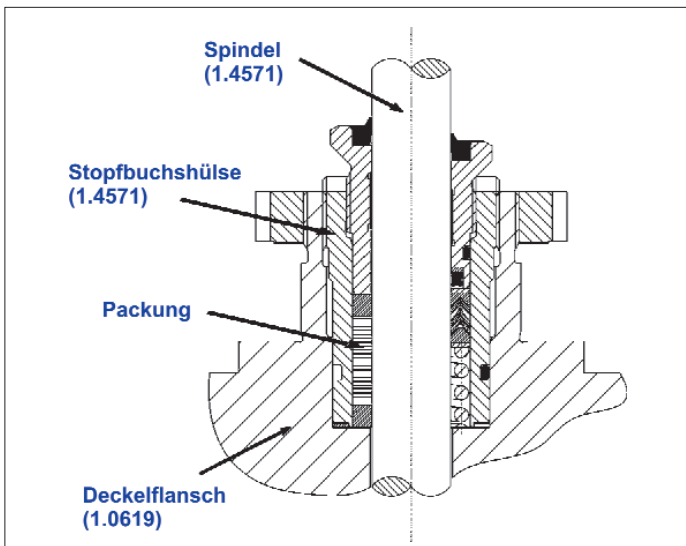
Korrosionsfeste Ausführung einer Ventilstopfbuchse
